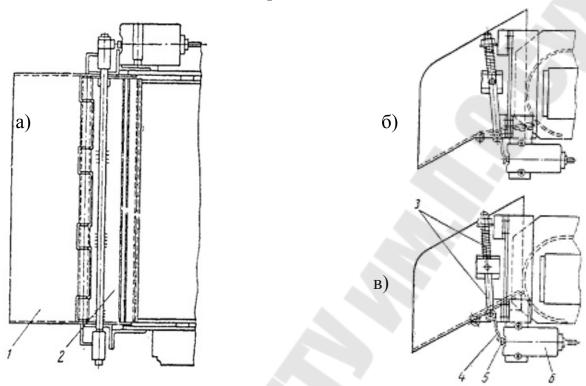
Предохранительное устройство с шарнирным козырьком:
